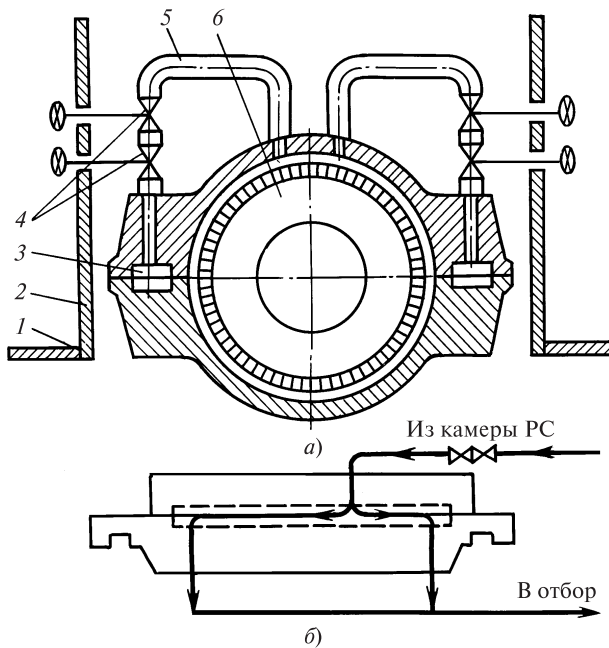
Система обогрева фланцев без внешних коробов *a* — поперечный разрез корпуса ЦВД по камере регулирующей ступени; *b* — схема потоков греющего пара; 1 — площадка обслуживания; 2 — обшивка турбины; 3 — обнизка; 4 — запорные вентили; 5 — трубопровод; 6 — камера регулирующей ступени
